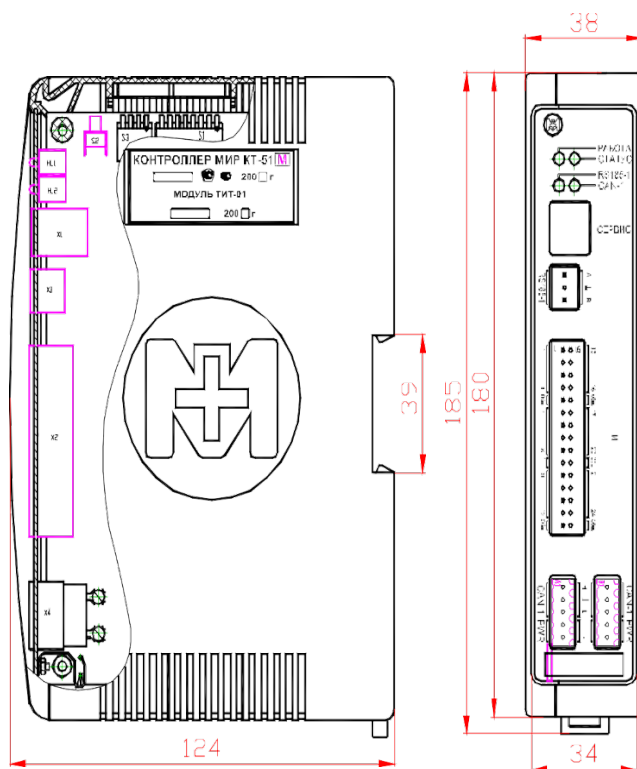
Внешний вид и габаритные размеры модуля ТИТ-01
